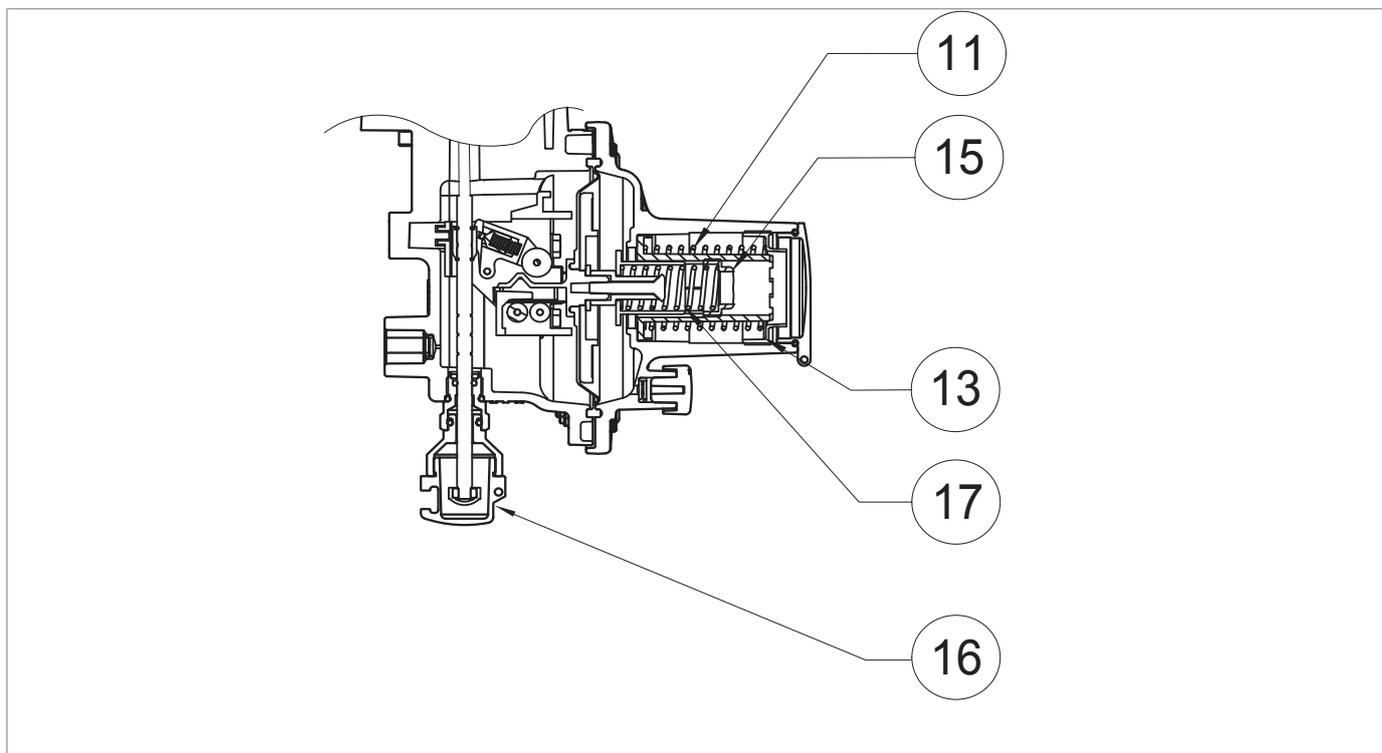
Калибровка реле давления для клапана блокировки LA
